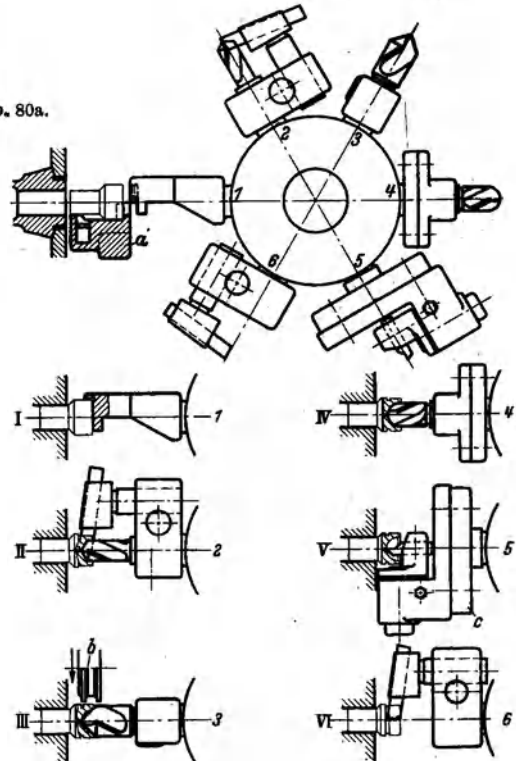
Arbeitsfolge für die Bearbeitung des Teiles Abb. 81. I. Das Arbeitsstück wird durch den Zubringer a des Magazins (vgl. auch Abb. 83) vor die Spindelmitte gebracht und durch den Einstoßer in Loch 1 in die Spannzange geschoben. II. Vorbohren der Kugelfanne und Überdrehen mit Tangentialstahl. III. Aufbohren der Kugelfanne und gleichzeitig Formen vom hinteren Querschlitten mit Rundstahl b. IV. Vorformen der Kugelfanne durch Formbohrer. V. Fertigdrehen der Kugelform mit Kugeldrehwerkzeug c (Abb. 84). VI. Fertigdrehen des Zapfendurchmessers mit Tangentialstahl.
